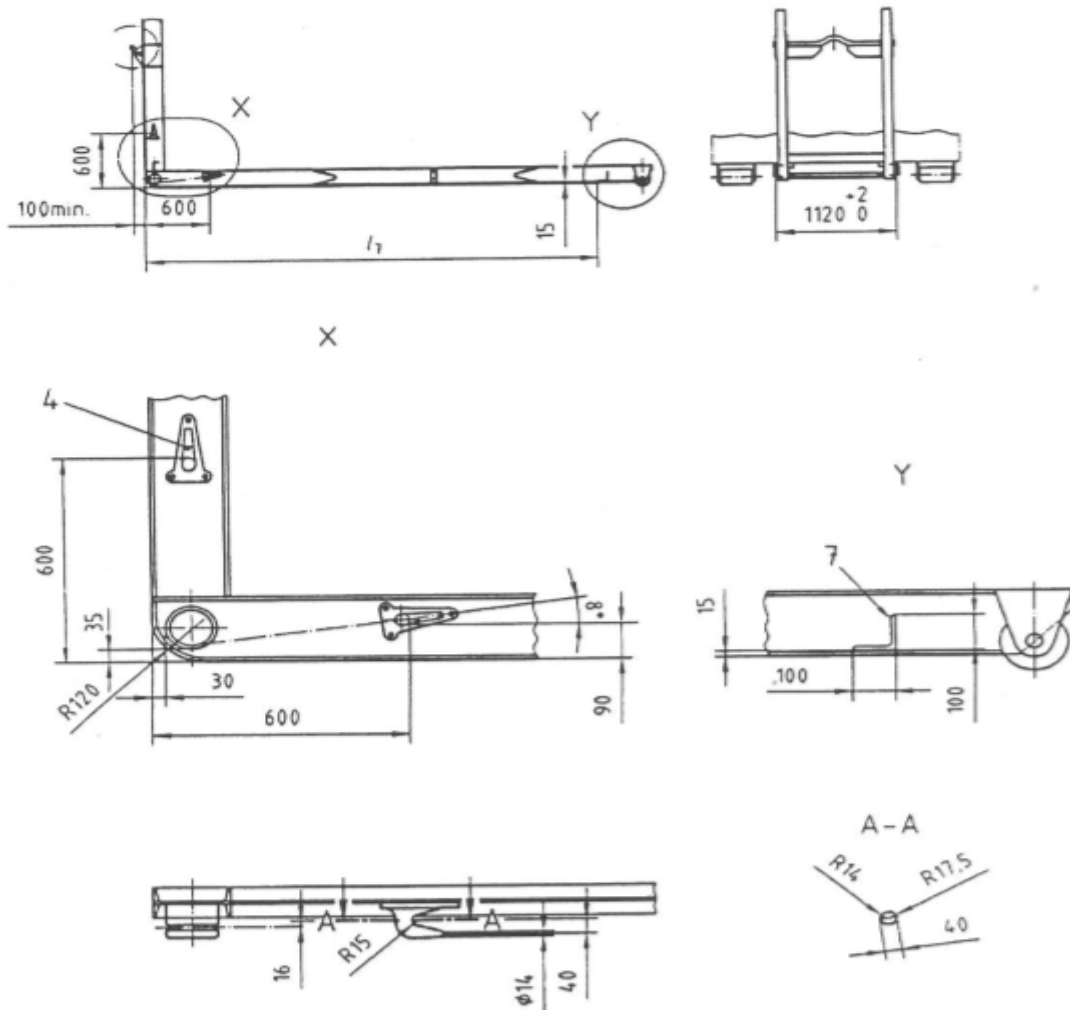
Všeobecné tolerance: ISO 2768 C[11]
